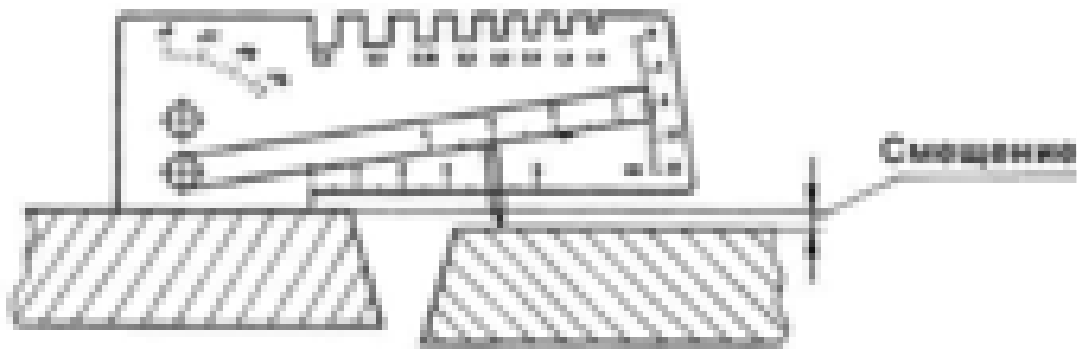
Схема измерения смещений при сварке швов
